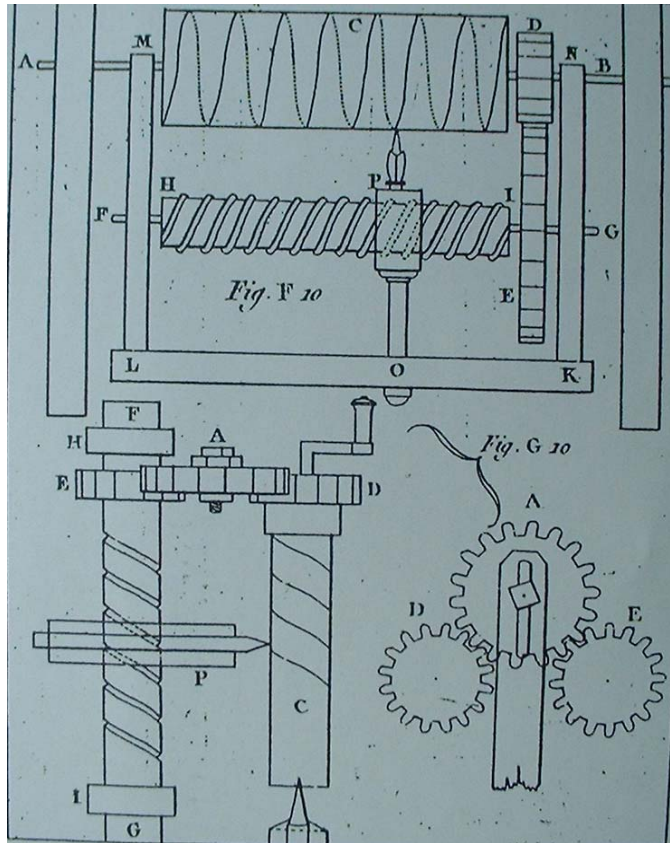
, page 172, planche8, Lanz et Bétancourt.
